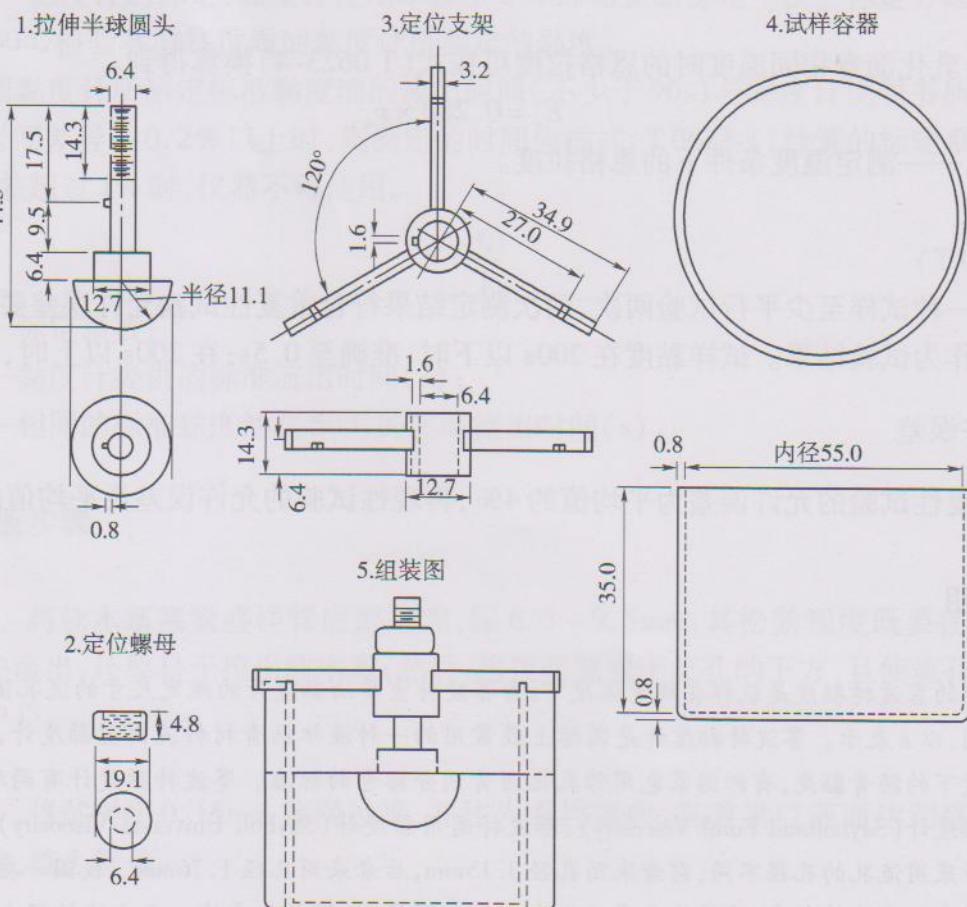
黏韧性试验器(尺寸单位:mm)
